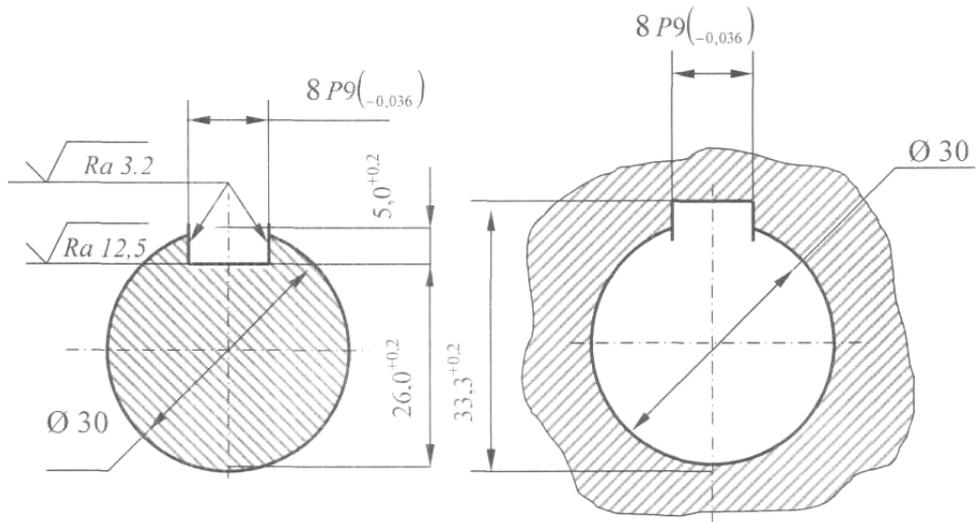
Обозначение допусков шпоночного соединения по ширине на детализованных чертежах
